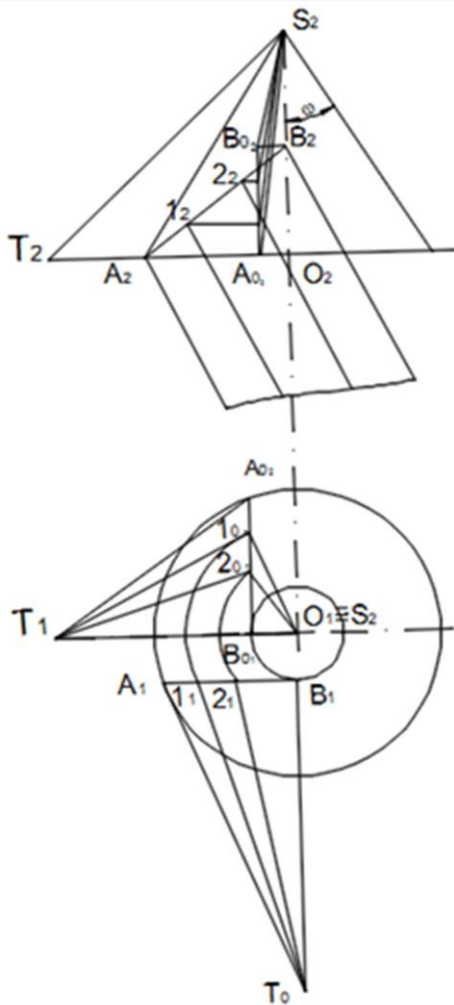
Профілізації фрези для обробки поверхні канавки свердла, утвореної рухом прямолінійної різальної кромки
